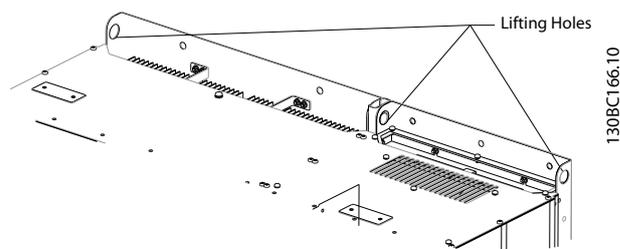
Рекомендуемый метод подъема, типоразмер D13
